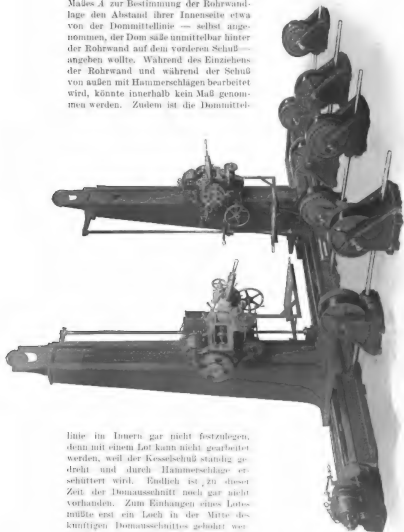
Langkesselbohrmaschine (Werkzeugmaschinenfabrik Collet & Engelhard).
